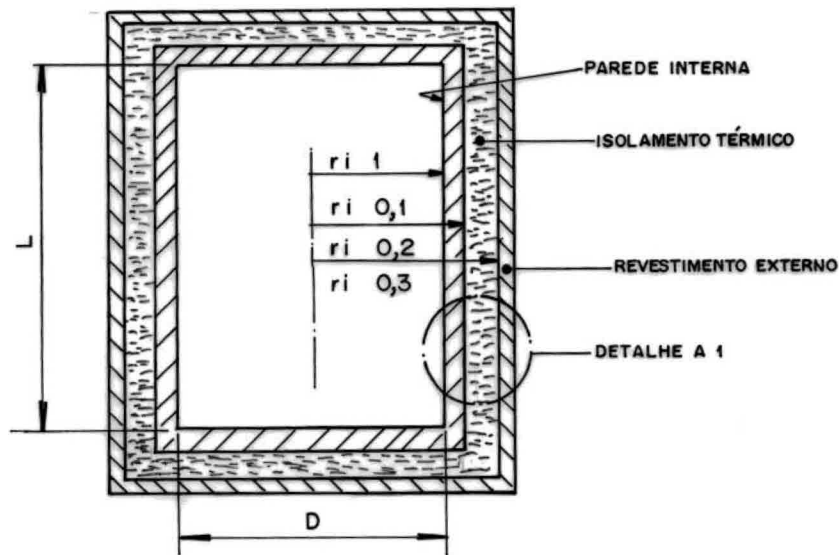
Tipo de construção do tanque de armazenamento.
